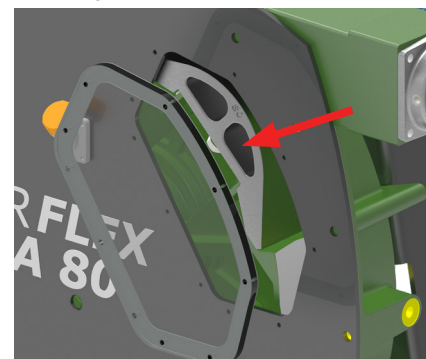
Entfernen Sie das Inspektionsfenster
